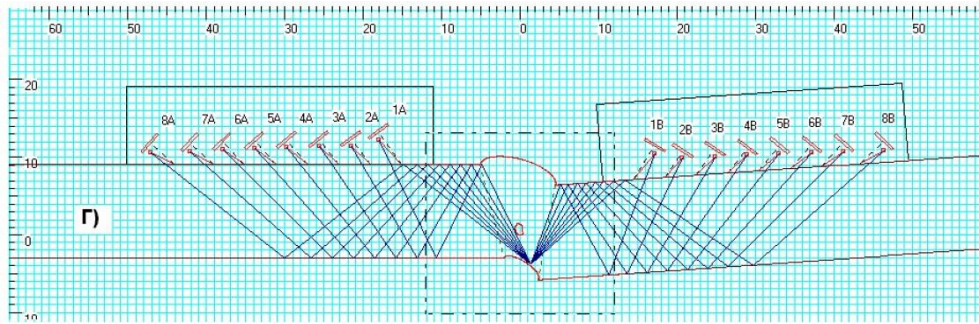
Прозвучування кореня зварного з'єднання двічі відбитими променями
